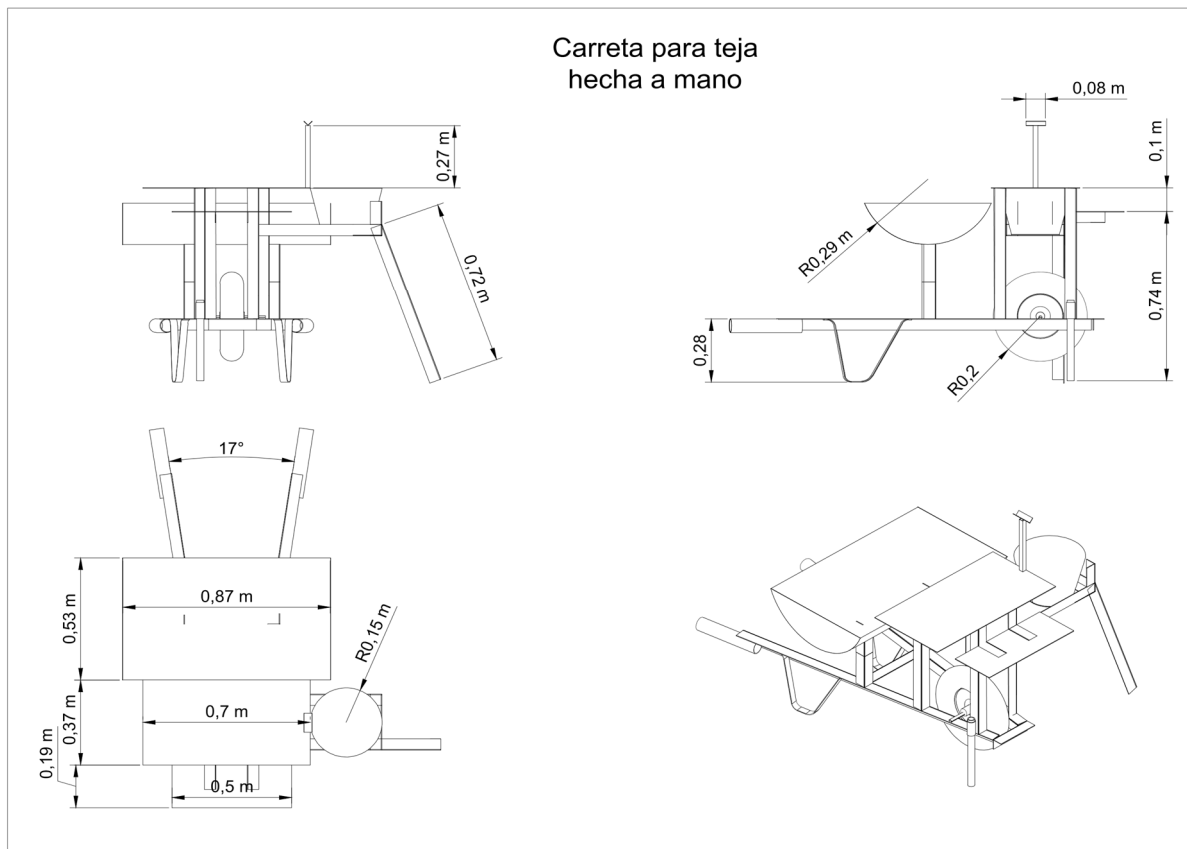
Plano carreta para teja hecha a mano. Elaborado por Juan Vivas Pedraza (2017).
